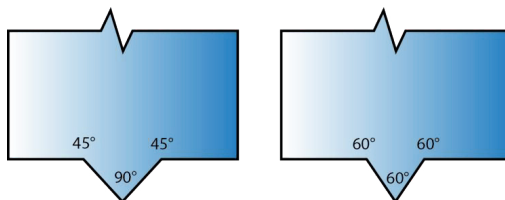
Schweißnaht (Polyfusion-Schweißen)
